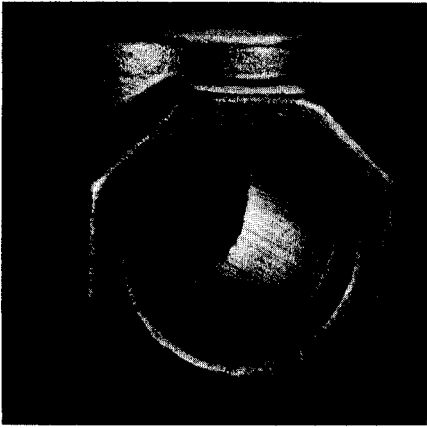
Kugelhahn-Gehäuse (4,35 kg), NW 50, aus C 35 Pb-N. Auf der äußeren Achteckkontur kann ein Schlüssel oder eine Rohrzange angesetzt werden. Durch Warmentgraten mit engem Schnittwerkzeug entsteht im Gratnahtbereich eine saubere Fläche. Die Bohrung wird scharf ausgeleuchtet, um das Bearbeitungsaufmaß in engen Grenzen zu halten.
